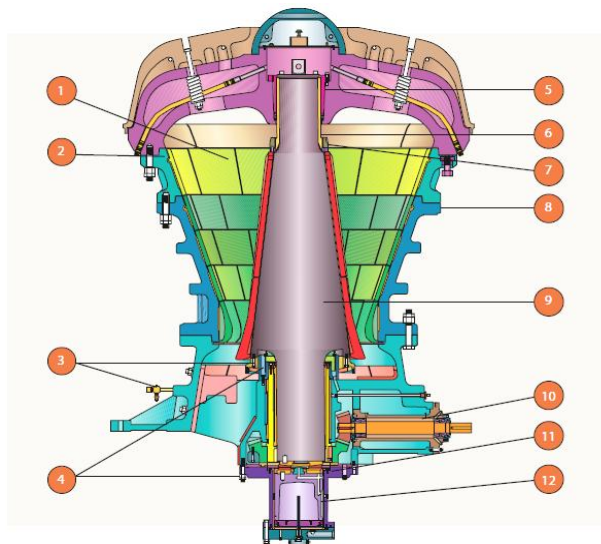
Дробарка Metso Superior МК-II 54-75: 1 – подрібнювальна камера; 2 – марганцева оболонка; 3 – ущільнювач пилу; 4 – урівноважувальний елемент; 5 – спайдер; 6 – невід'ємний головний вал; 7 – головна гайка з вогневого кільця; 8 – високоміцний корпус; 9 – головний вал; 10 – зовнішній передавач і регулятор люфту шестерні; 11 – індикатор зносу підшипника; 12 – основна система положення валу
